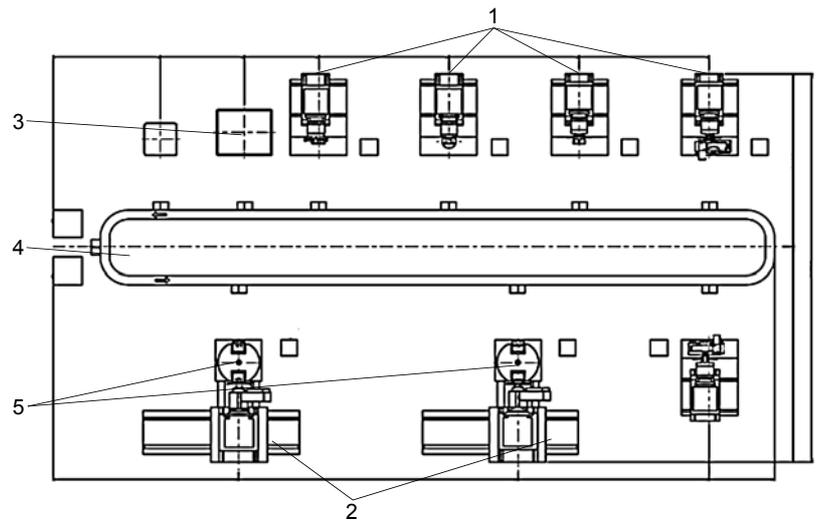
Схема прямоточной линии для дифференцированной обработки типовых поверхностей лопаток: 1 — одношпиндельные шлифовальные центры; 2 — двухшпиндельные шлифовальные центры; 3 — координатно-измерительная машина; 4 — транспортная система; 5 — модуль обработка/загрузка
